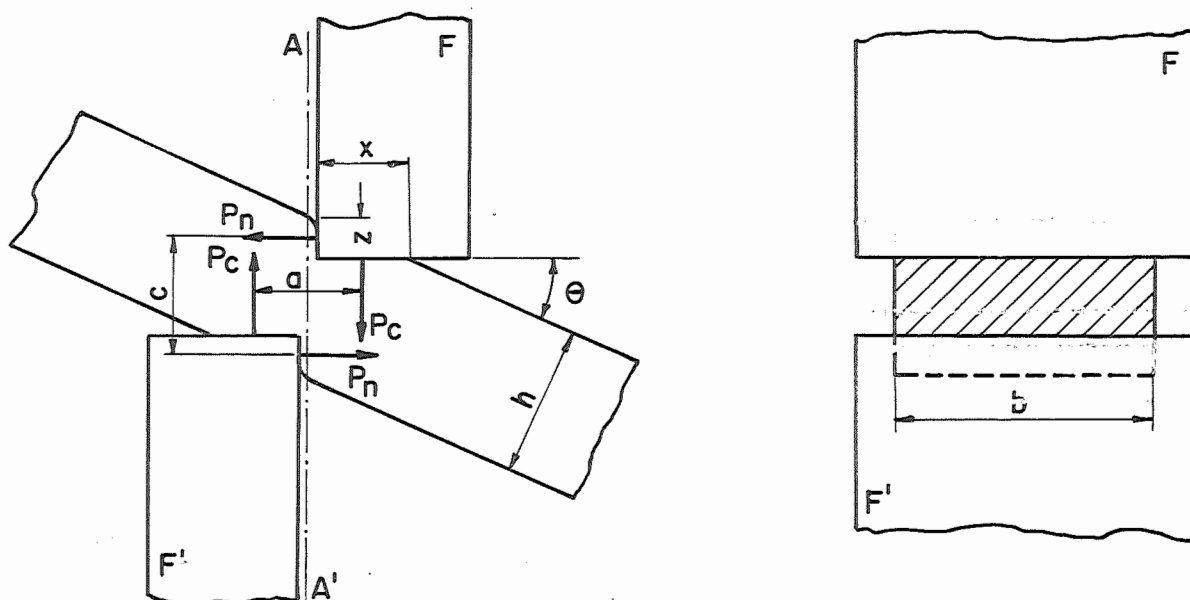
Corte em chapas através de facas paralelas de secção retangular.
